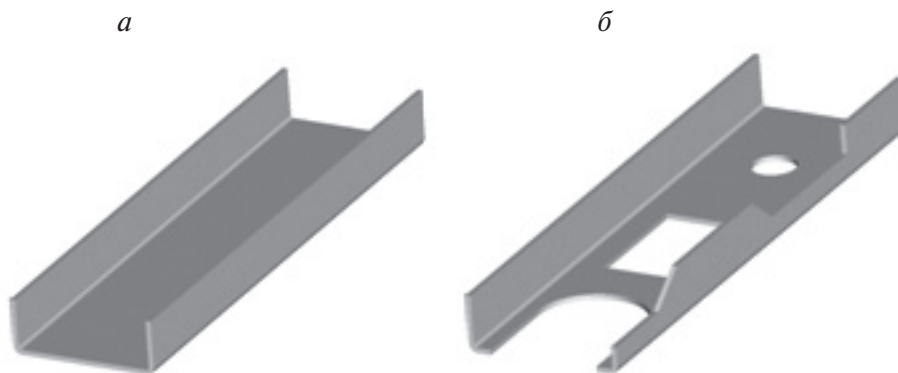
Создание базовой заготовки (*а*) и окончательный вид модели (*б*)
